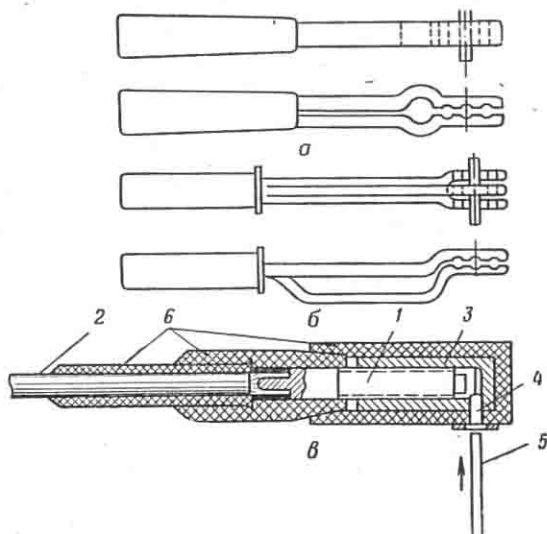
Электродержатели для дуговой сварки и резки:
